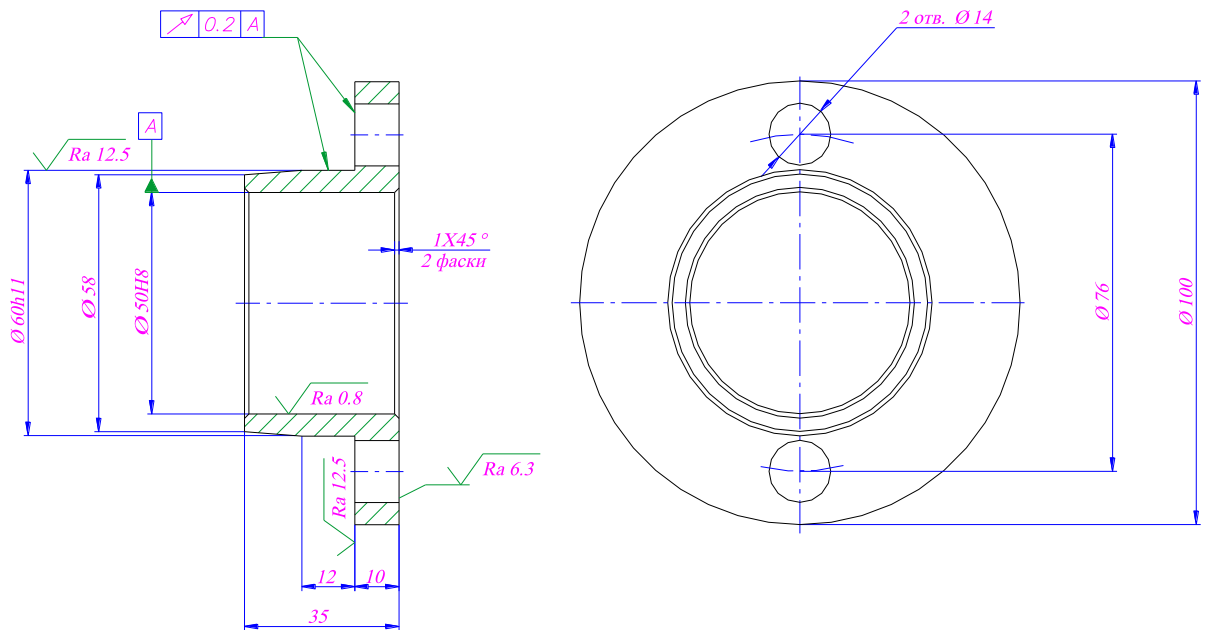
Конструкція деталі «Ступиця ведучої зірочки»
